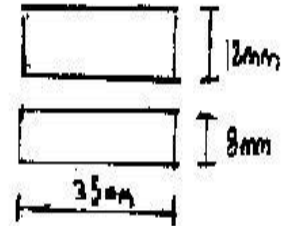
Boceto del diseño final del calentador con celdas de combustible, detallando piezas que serán utilizadas para su fabricación, parte 2.
